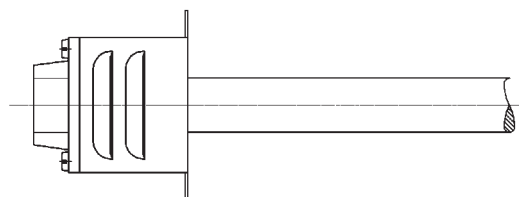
Anschlussvariante Ausführung Q mit KO 110/T200
